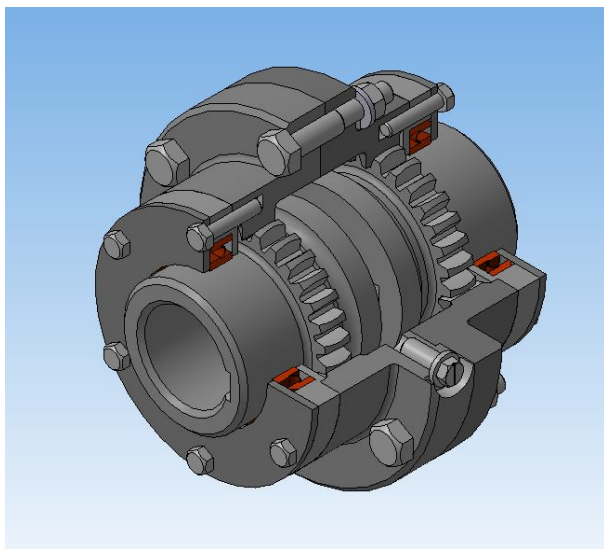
Вид двухвенечной зубчатой муфты Рис.11 Конструкция двухвенечной зубчатой муфты
